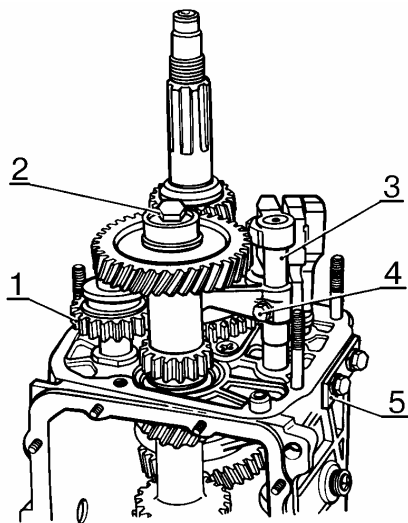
Отворачивание болтов крепления блока шестерен и вилки включения V передачи и заднего хода:
